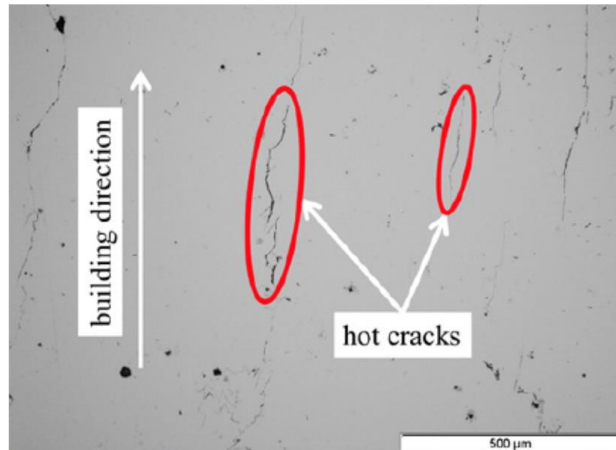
Fisuras en caliente formadas en la SLM AA-7075 a lo largo de la dirección de fabricación [69].
